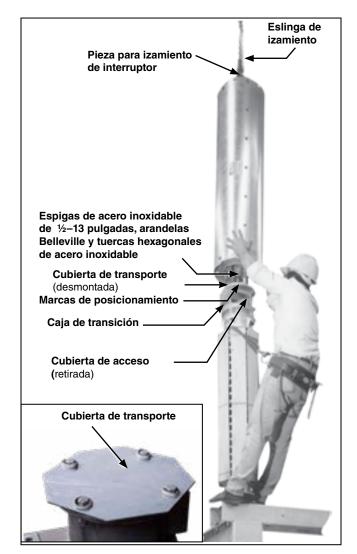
Ensamblaje del interruptor a la columna de soporte aislante.
